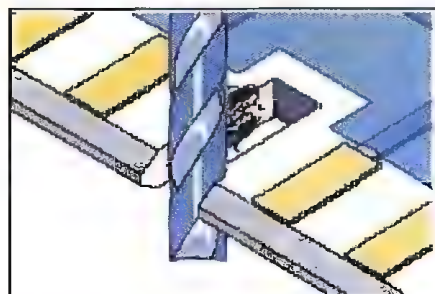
Фрезеровать поврежденный участок твердосплавной торцевой фрезой
